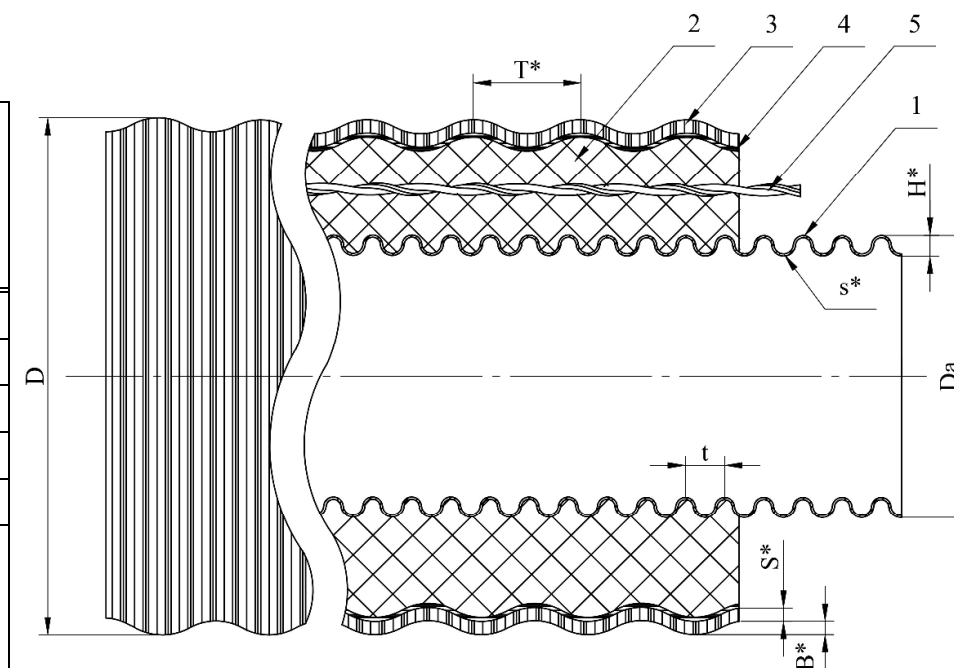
Конструкция и основные размеры труб СТИЛФЛЕКС
